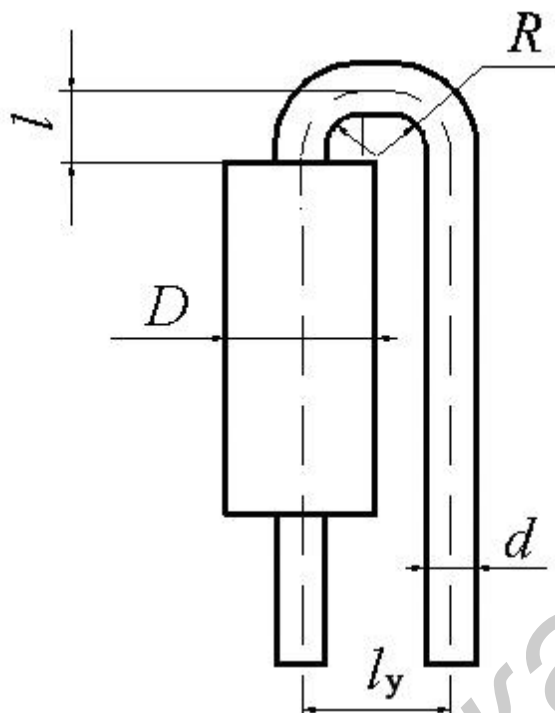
Обозначение установочного размера  $l_y$  для исполнения 22
